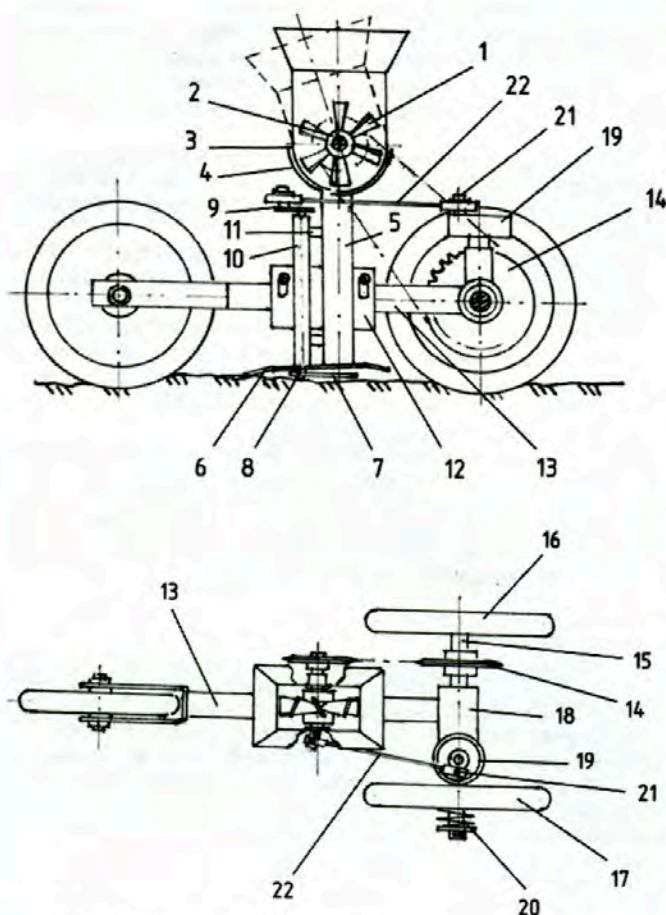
Схема устройства аппарата для широкополосного высева семян
